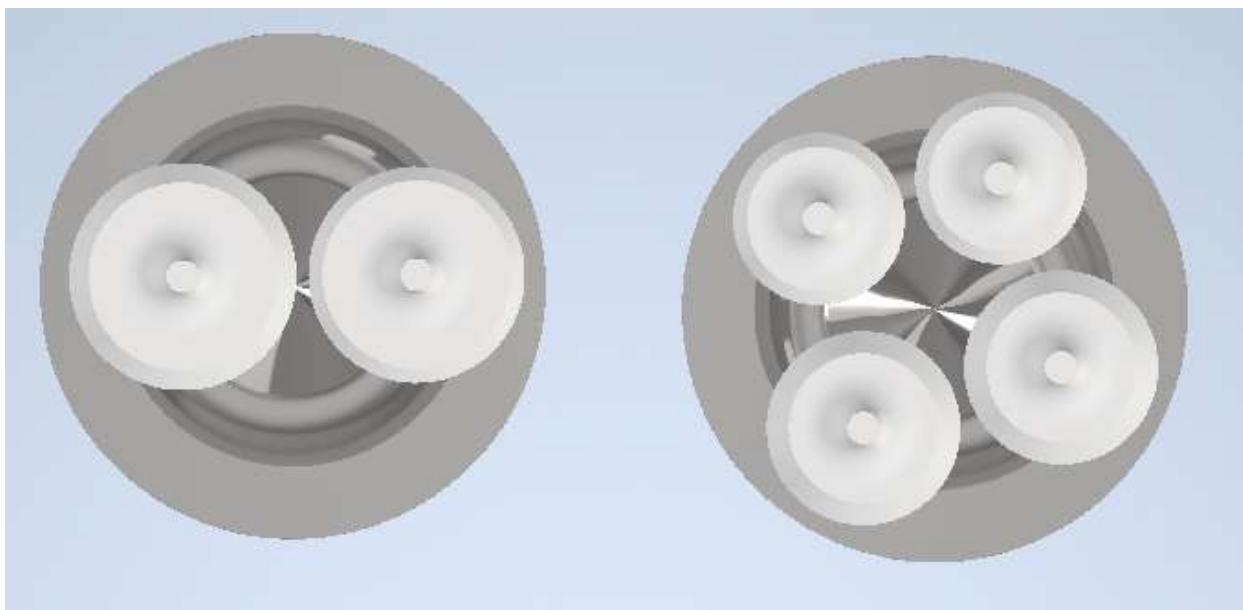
Эскизная компоновка двух и четырех клапанов в ГБЦ в SolidWorks
